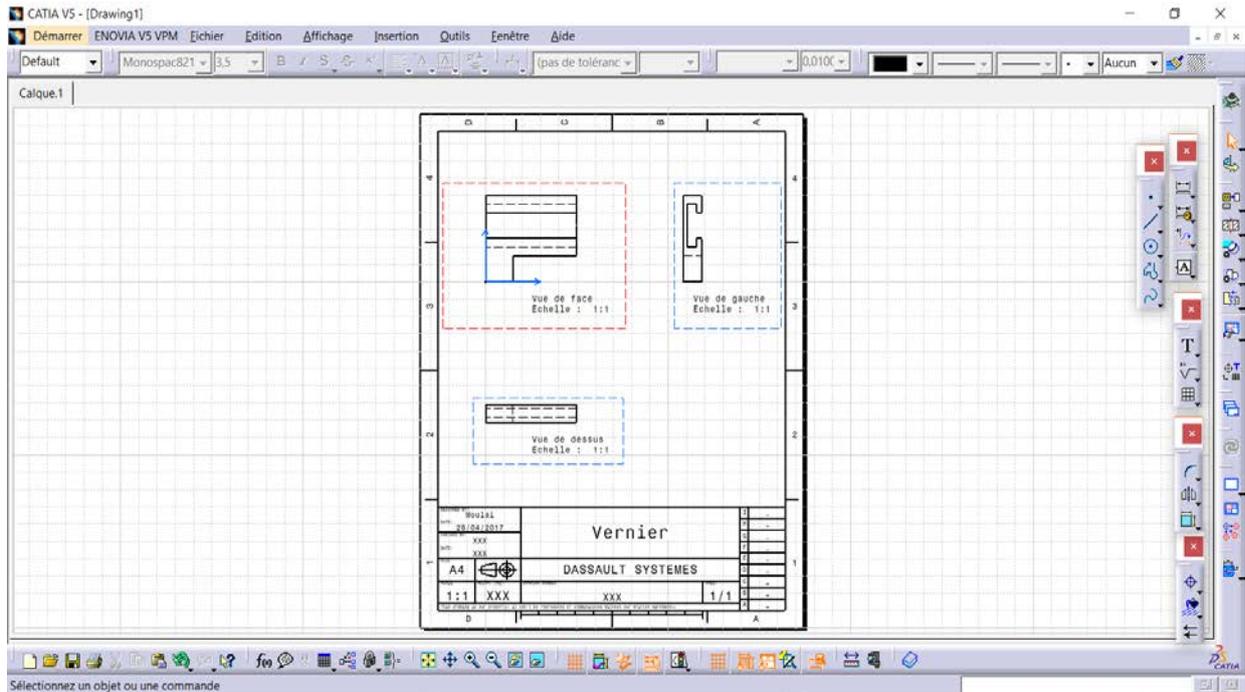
Drafting (mise en plan 2D) du vernier de l'assemblage Pied à coulisse [1], [2]
